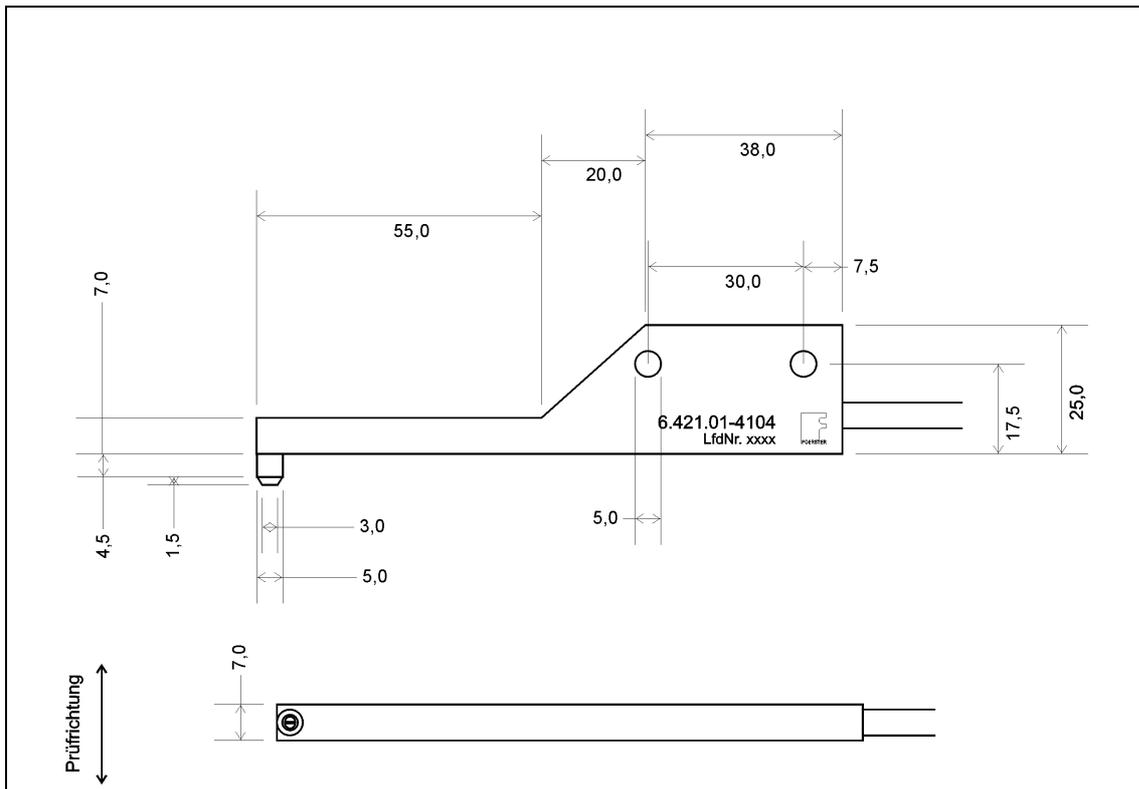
Taster abgewinkelt 90 D, AK 6.421.01-4104.
